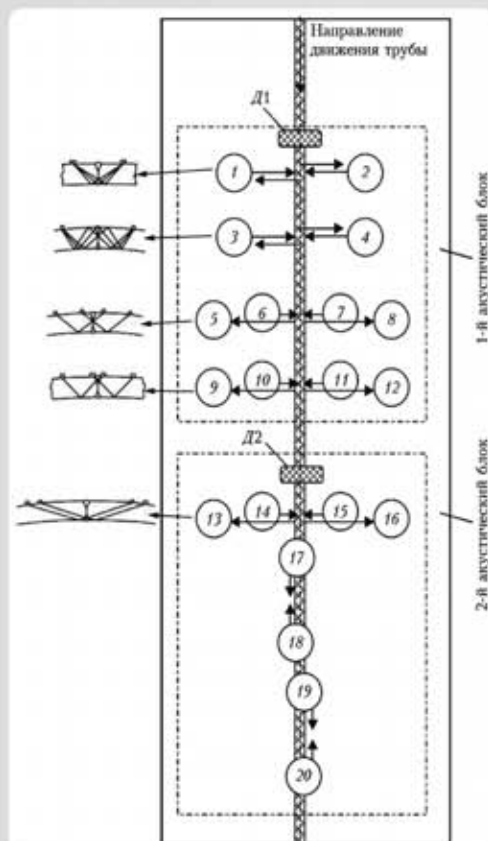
Схема расположения акустических головок при контроле продольных сварных соединений: D1, D2 — лазерные датчики слежения за валиком усиления сварного шва; 1 - 4 — группа наклонных ультразвуковых преобразователей для контроля на продольные дефекты; 5 - 16 — ультразвуковые преобразователи, работающие в схеме типа «тандем»; 9 - 16 — ультразвуковые преобразователи, стоящие на сварном шве и работающие в иммерсионном варианте на обнаружение поперечных дефектов
